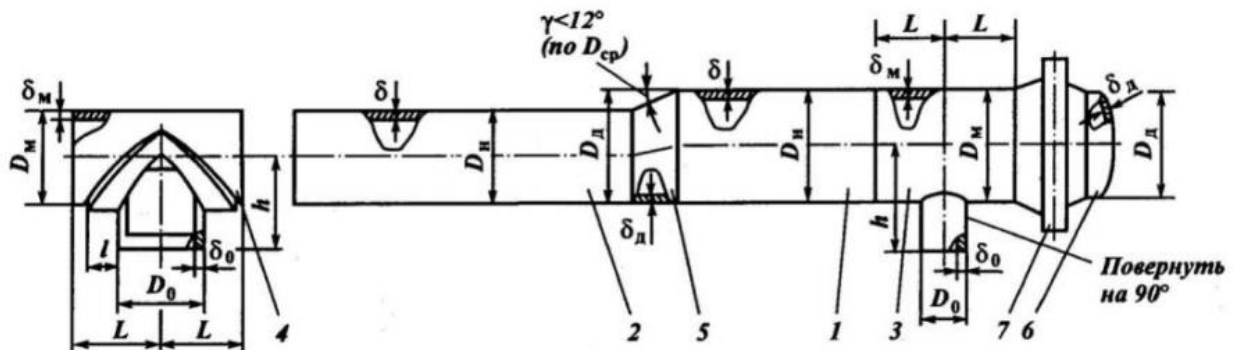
Схема КПП СОД: 1,2- обечайка корпусная; 3- тройник корпусной; 4- тройник равнопроходный; 5- переходник эксцентрический; 6- днище крышки затвора; 7- затвор.
